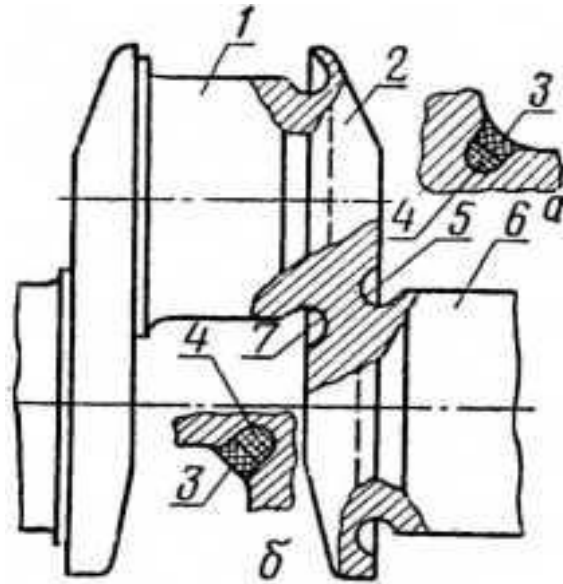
Підготовка тріщини на шийках колінчастого валу двигуна для зварювання:
